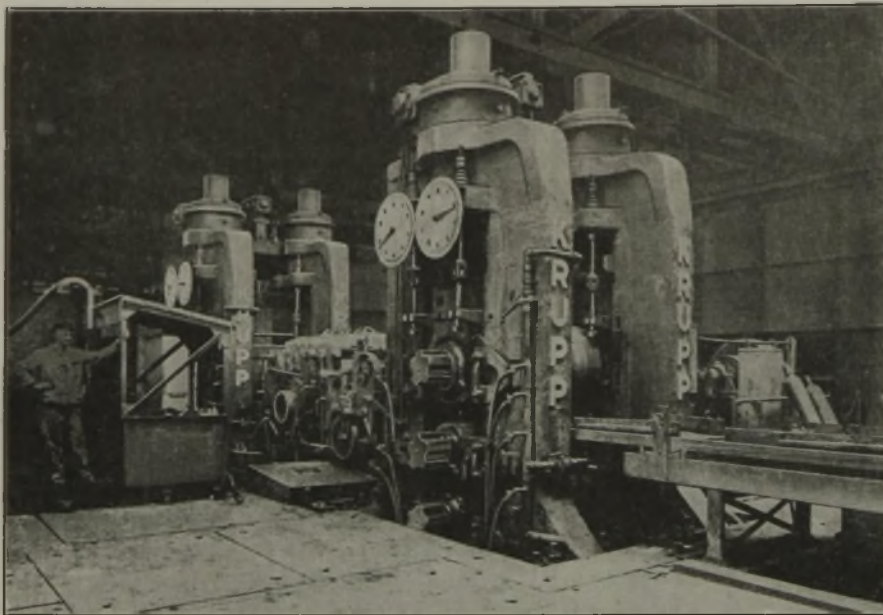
Erstaussführung des Röchling-Walzwerkes.
